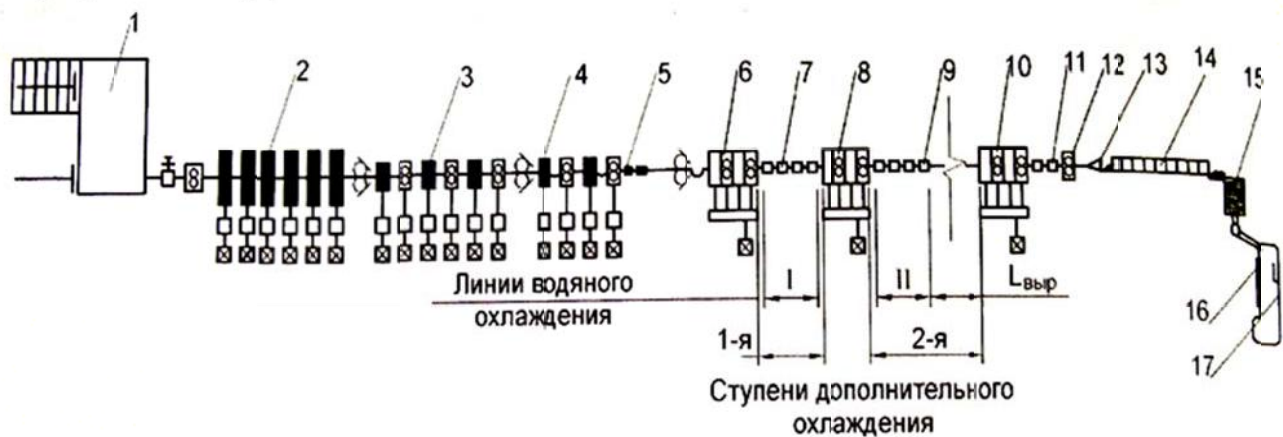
Схема расположения основного технологического оборудования высокоскоростного проволочного стана нового поколения для прокатки катанки широкого размерного и марочного сортамента:
